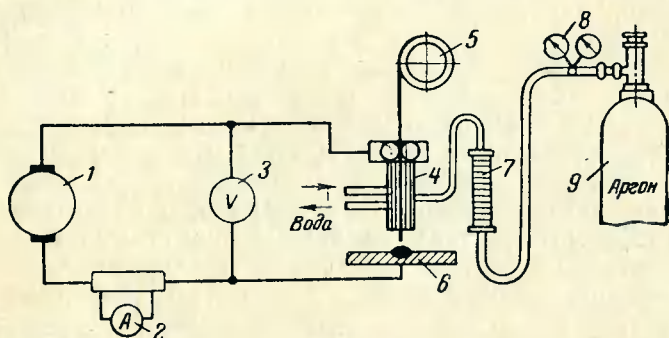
Схема поста аргоно-дуговой сварки плавящимся электродом.
